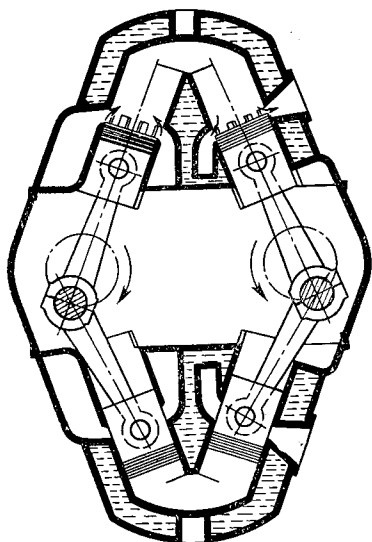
Схема двухвального двигателя с цилиндрами, расположенными под углом, и двумя камерами сгорания
